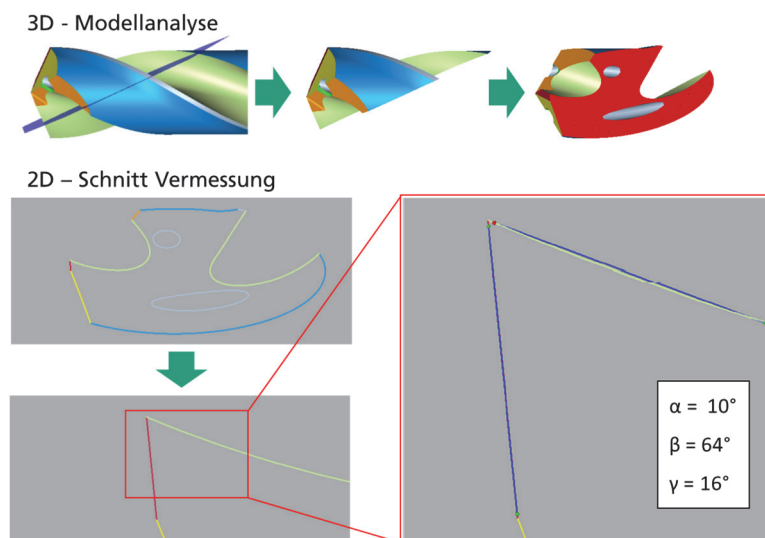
Herleitung der Werkzeuggeometrie (Bilder: Wolf GmbH)
